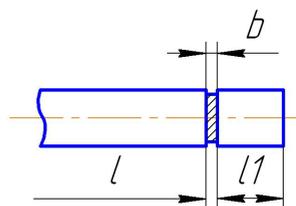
Ширина реза при отрезке проката: L – длина прутка; l – длина заготовки; b – ширина реза
